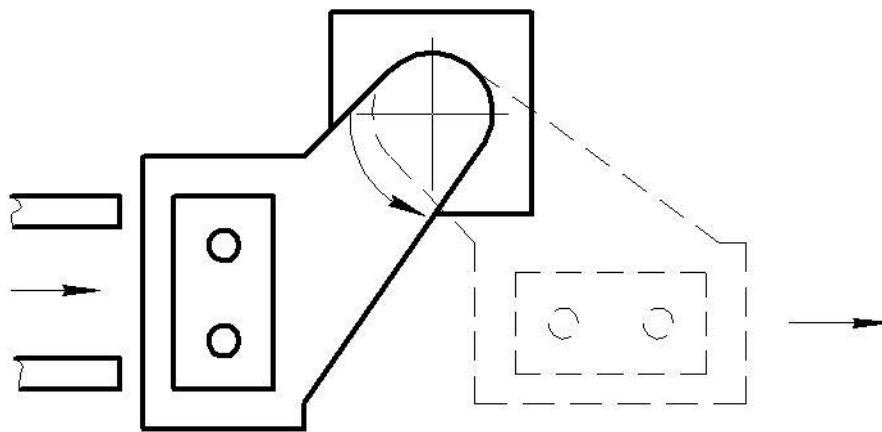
Схема спрацьовування поворотного столу, який здійснює поворот заготовок на 90°
